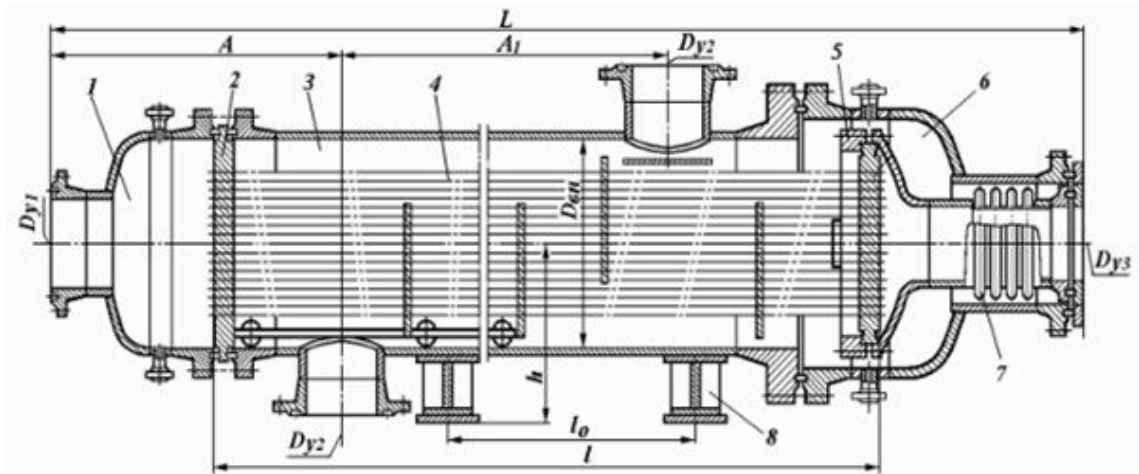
Нежорсткий кожухотрубний теплообмінник. Версії з сільфонним компенсатором: 1 – роздавальна; 2 – трубна плита; 3 – корпус; 4 – труба; 5 – плаваюча головка; 6 – задня кришка; 7 – компенсаційний сільфон; 8 - опора.
